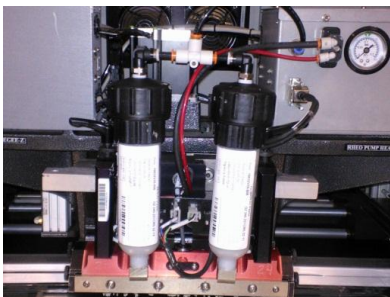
Bomba Neumática y jeringas de soldadura de pasta [SKWS]
